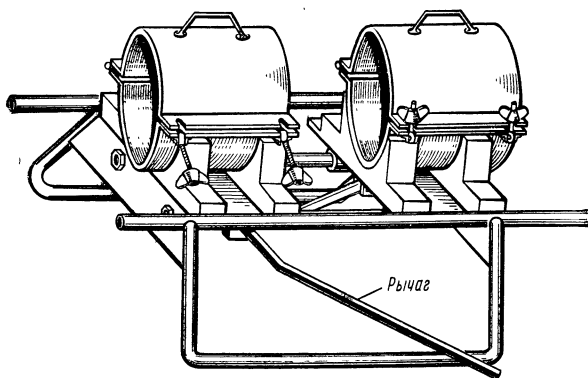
Станок для соединения полиэтиленовых труб методом стыковой сварки
